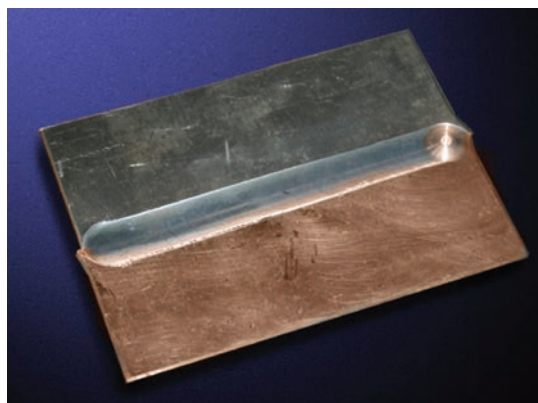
Сварка листов из алюминиевого сплава и меди.
